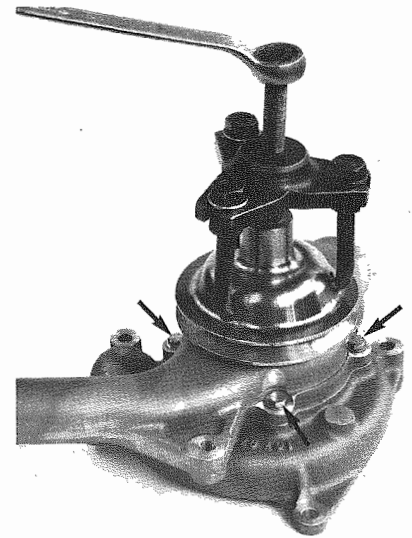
Estrattore n. 19 - Viti fissaggio
